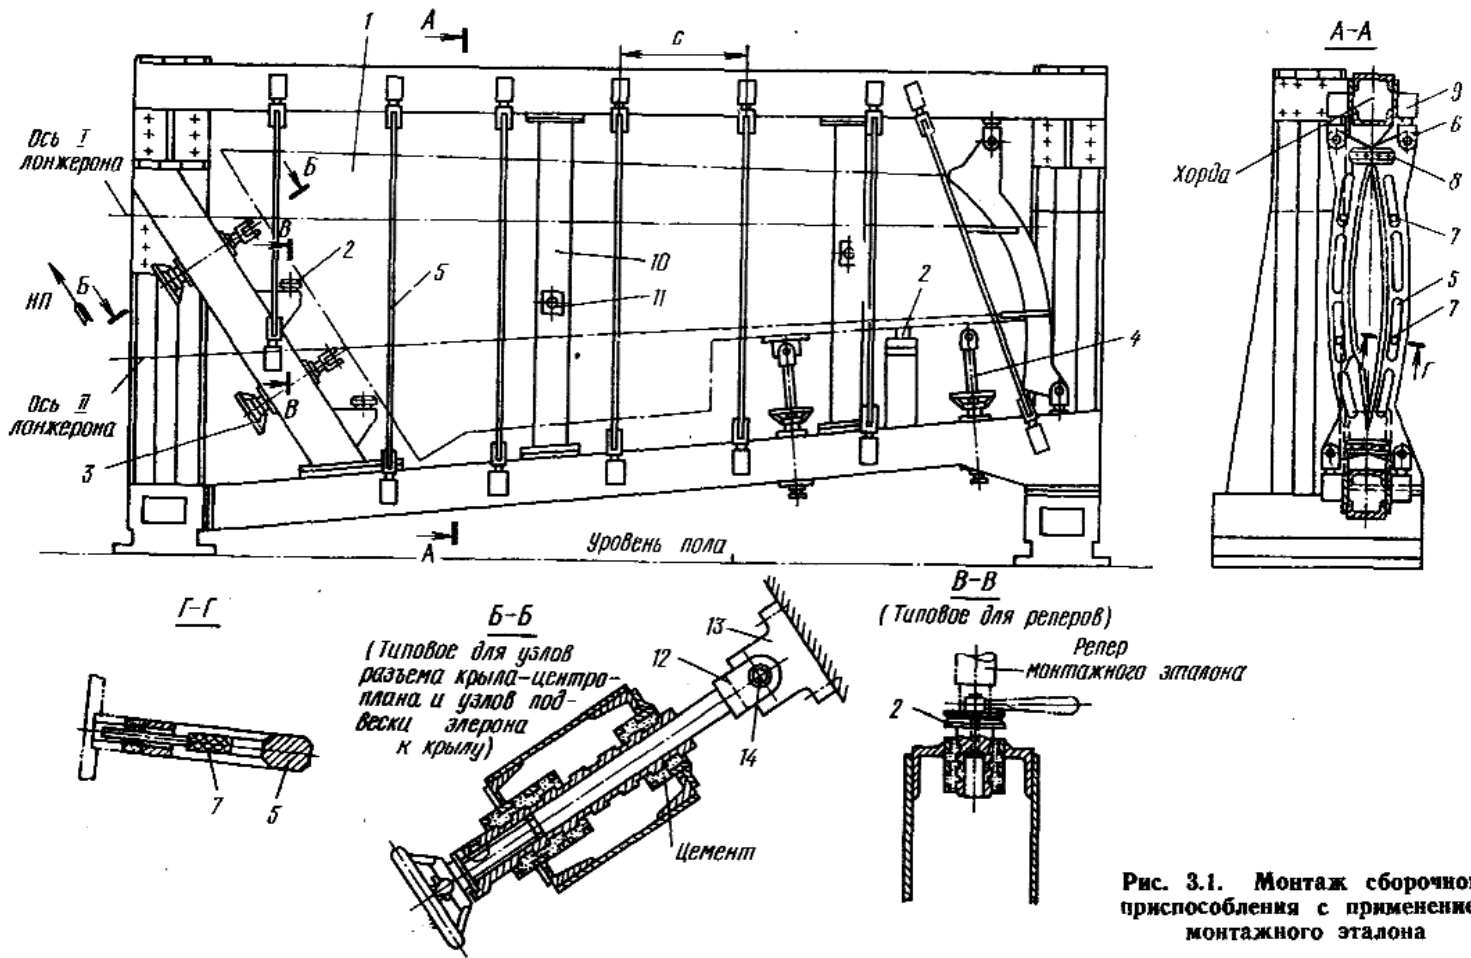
Монтаж сборочного приспособления с применением монтажного эталона
